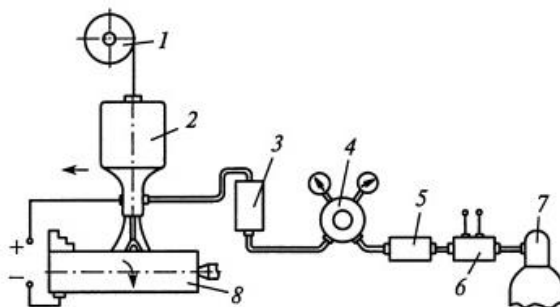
Схема установки для дуговой наплавки в среде углекислого газа [2]:
